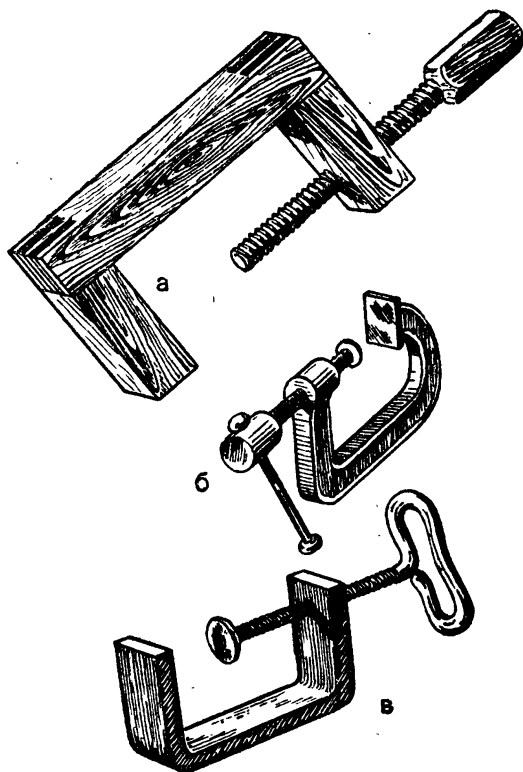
Приспособления для запрессовывания склеенных деталей:
